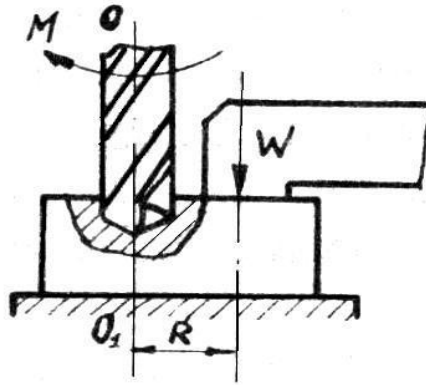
Схема розрахунку затискних зусиль при обробці заготовок на свердлильних верстатах
